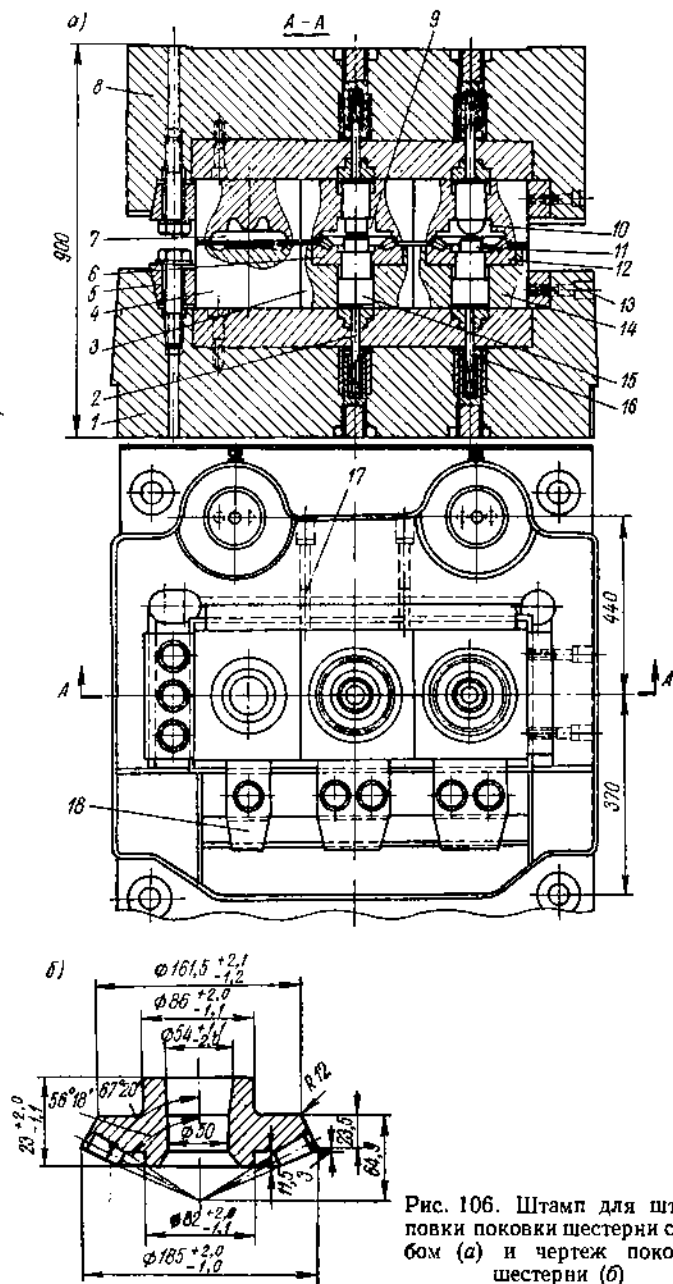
Штамп для штамповки поковки шестерни с зубом (а) и чертеж поковки шестерни (б)
